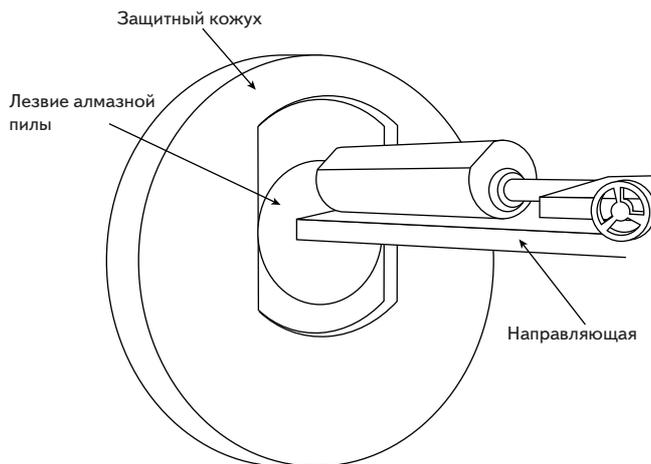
При изготовлении процессора заготовка разрезается алмазной пилой более чем на тысячу круговых подложек
